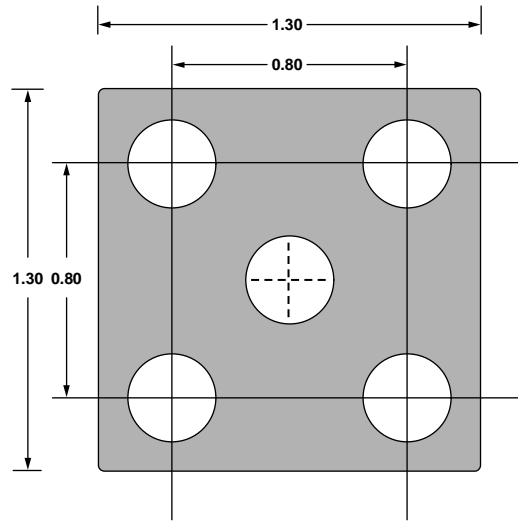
推荐的PCB热焊盘尺寸(mm)
